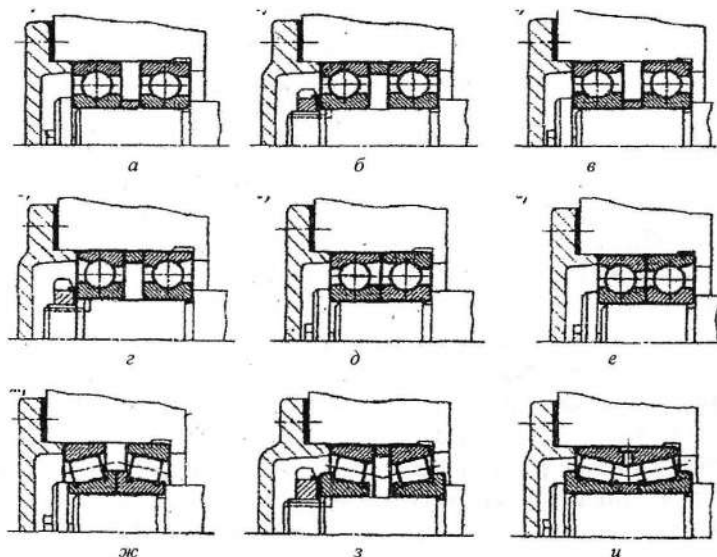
Фиксирующая опора с двумя подшипниками
